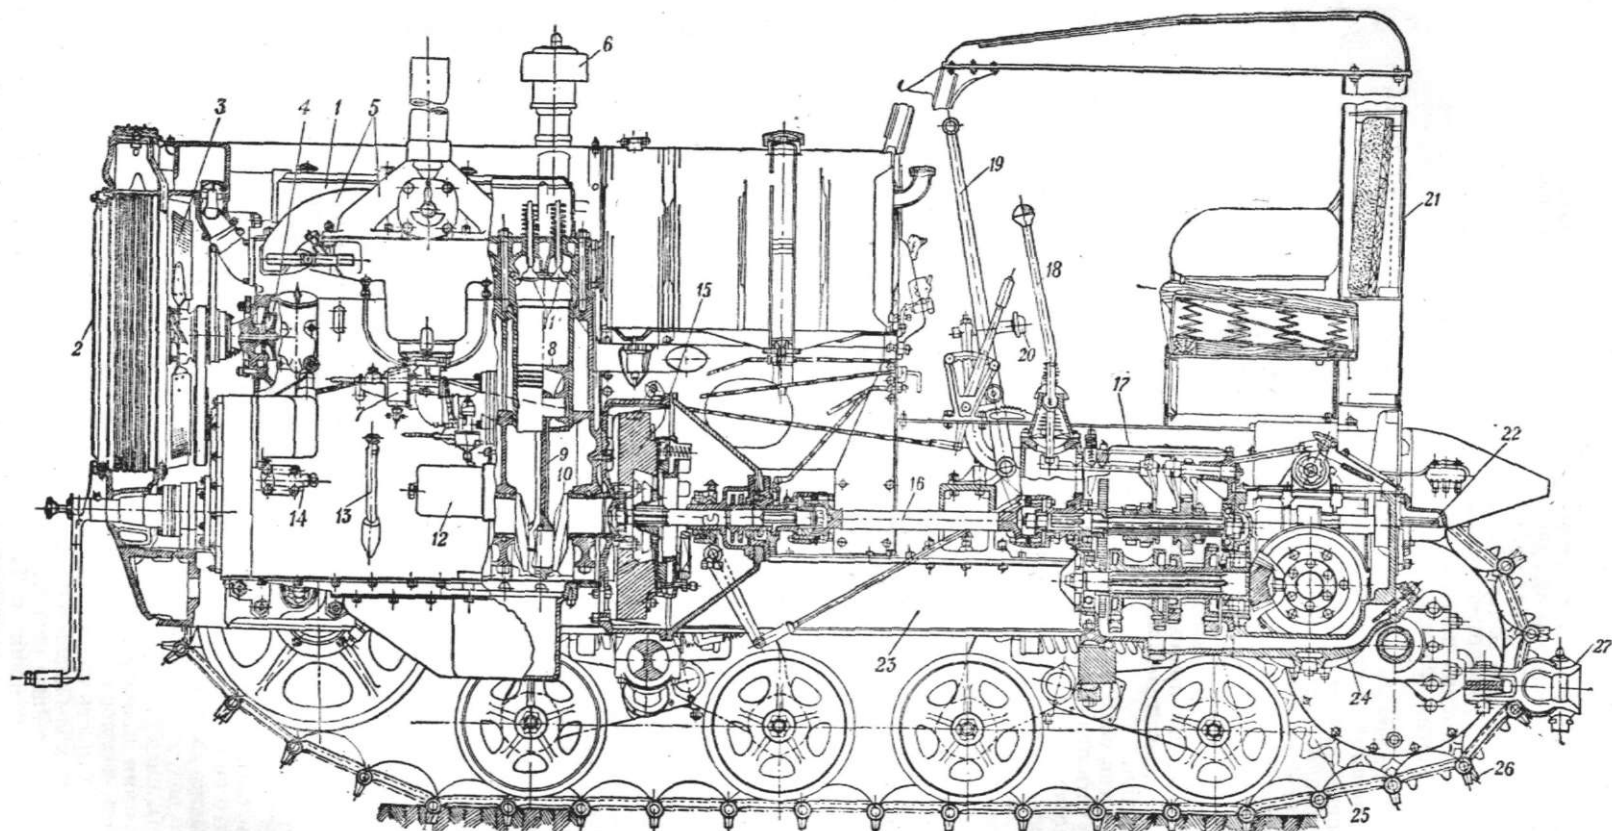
Продольный разрез трактора СХТЗ-НАТИ: 1—двигатель; 2—радиатор; 3—вентилятор; 4—помпа системы охлаждения; 5—выхлопные и всасывающие трубопроводы; 6—воздухприёмная труба воздухоочистителя; 7—карбюратор; 8—поршень; 9—шатун; 10—коленчатый вал; 11—клапаны; 12—масляный фильтр; 13—щуп для контроля уровня масла; 14—перепускной клапан; 15—механизм с монтированной на нём муфтой сцепления; 16—карданный вал; 17—коробка передач; 18—рычаг переключения коробки передач; 19—рычаг управления и торможения; 20—педаль для выключения муфты сцепления; 21—кабина; 22—вал отбора мощности; 23—рама трактора; 24—валный мост трактора; 25—ведущая вращающаяся; 26—гусеничная цепь; 27—прицепной крюк.
